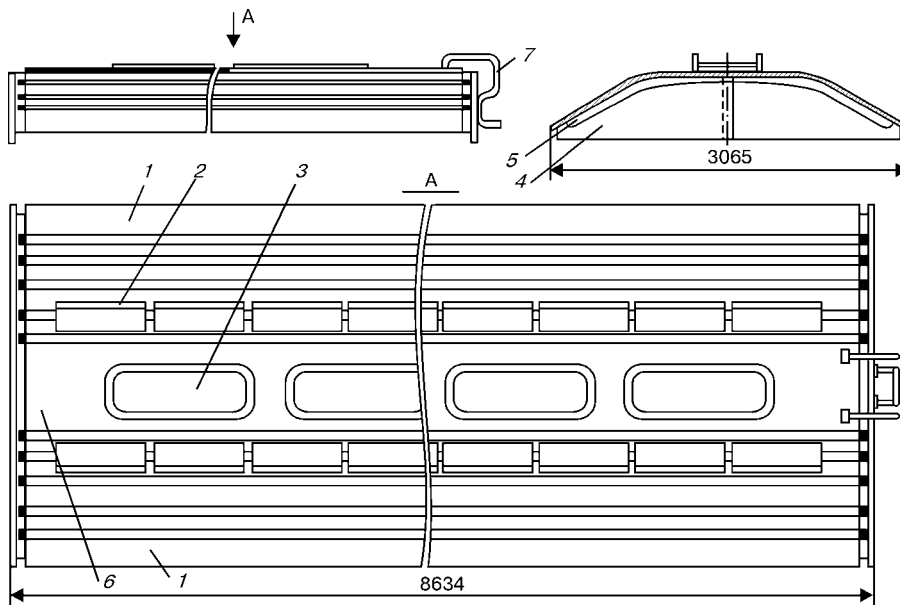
Крыша вагона-минераловоза: 1 – лист крайний; 2 – настил; 3 – крышка загрузочного люка; 4 – фрамуга; 5 – дуга; 6 – лист средний; 7 – поручень
